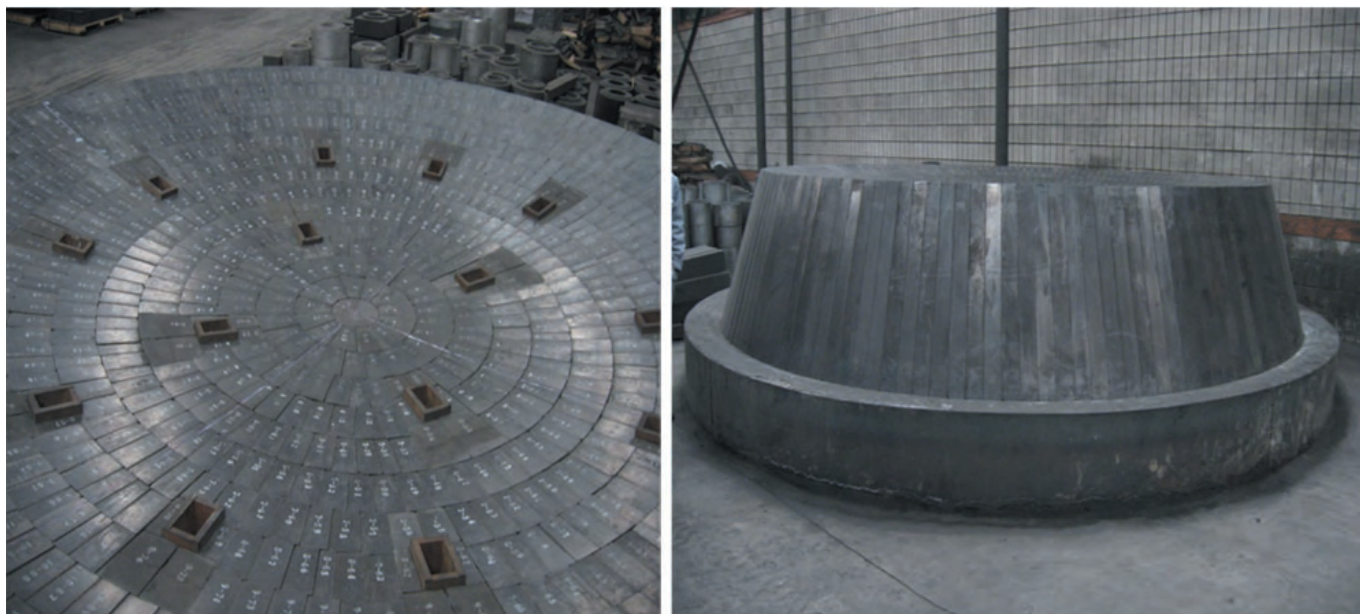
Пример стеновой сборки футеровки дна конвертера
